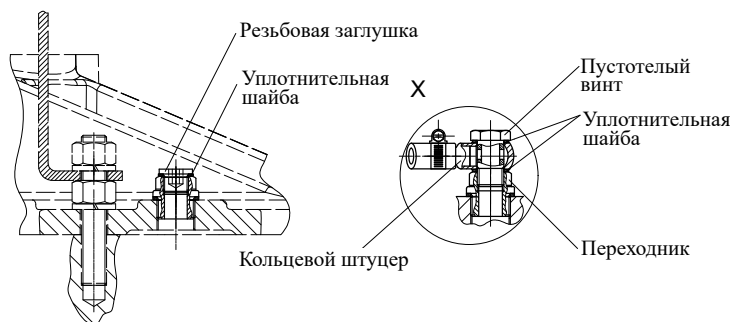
Крепление соединительного шланга к корпусу редуктора
